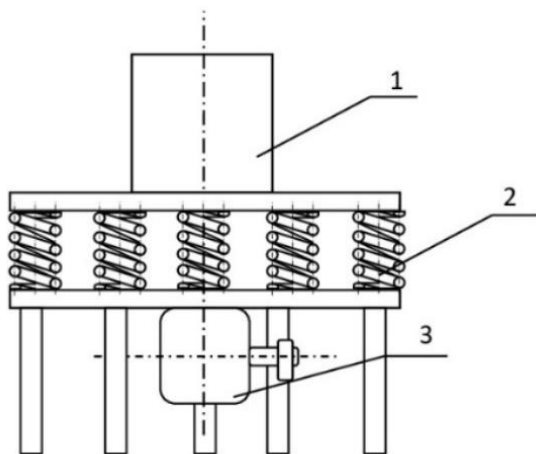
Схема лабораторної вібро-абразивної установки
